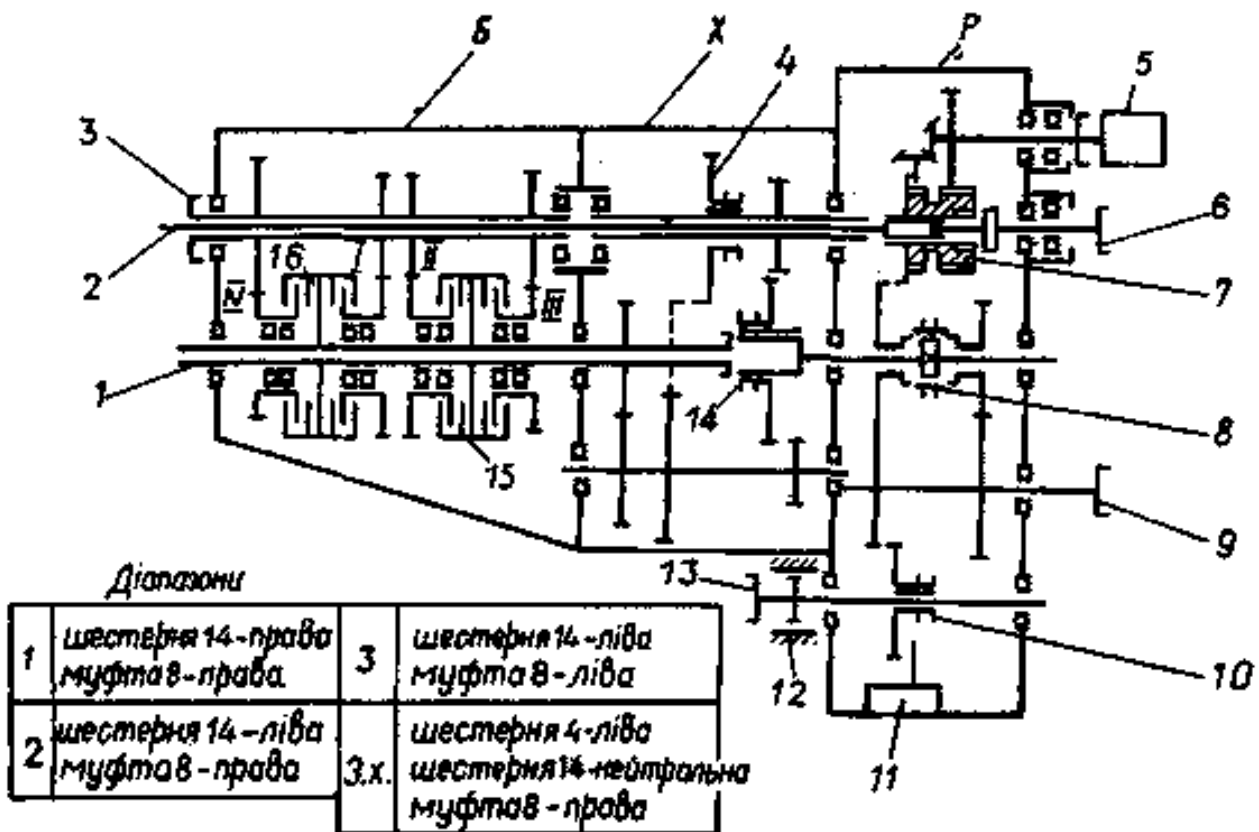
Кінематична схема коробки передач трактора Т-150К:
